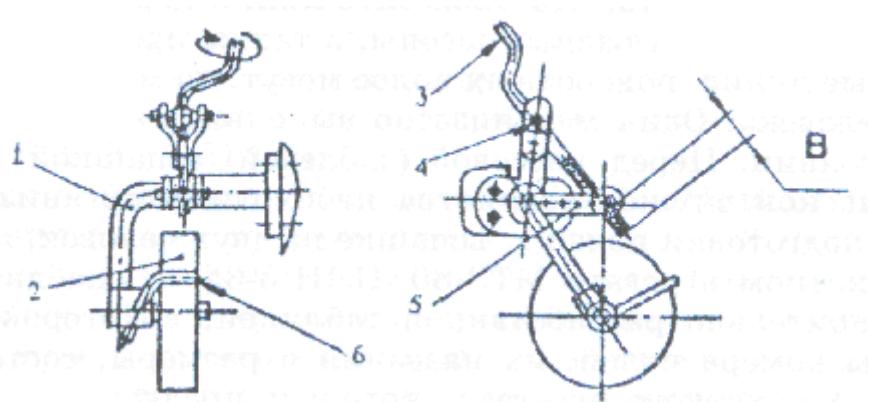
Опорное колесо с механизмом регулирования глубины
